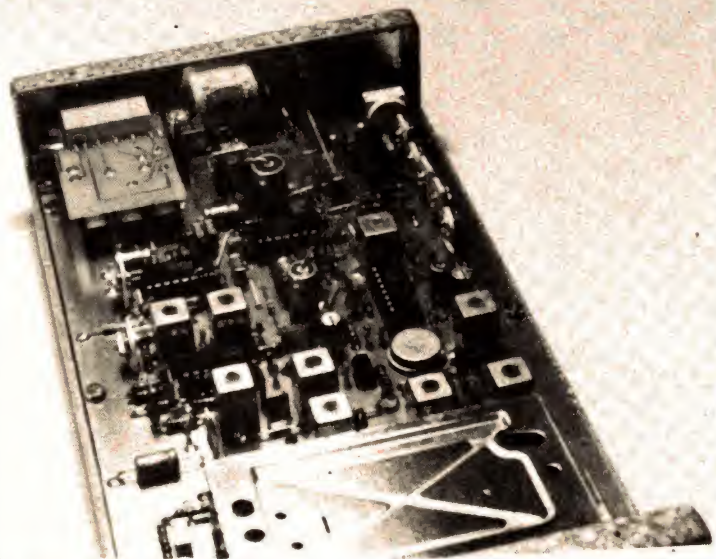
Photo E. - Vue de l'arrière. Remarquer le circuit imprimé K, soudé sur le commutateur.
